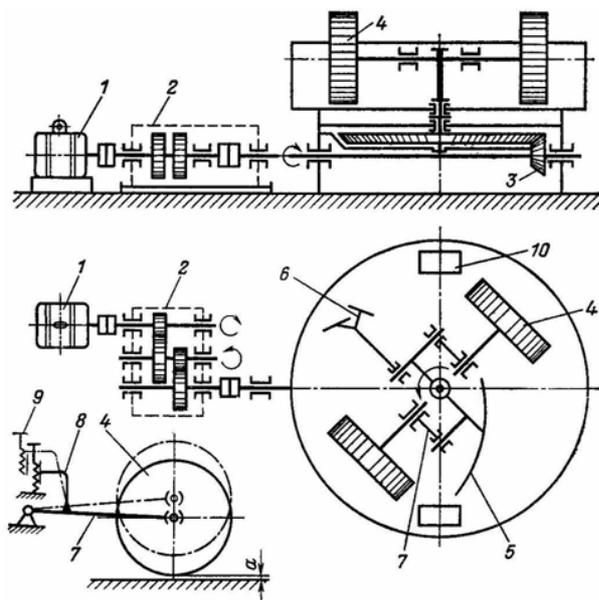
Кинематическая схема катковых смесителей: 1 - электродвигатель; 2 - редуктор; 3 - конические шестерни; 4 - катки; 5 и 6 - плужки; 7 кривошип; 8 - кронштейн кривошипа; 9 - регулирующий винт; 10 - разгрузочные дверки дна чаши
